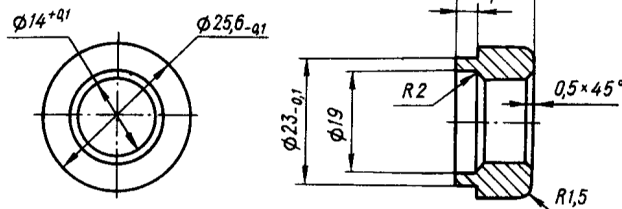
Оправка для выпрессовки и запрессовки втулки вала сошки рулевого механизма и втулок кронштейна маятникового рычага
